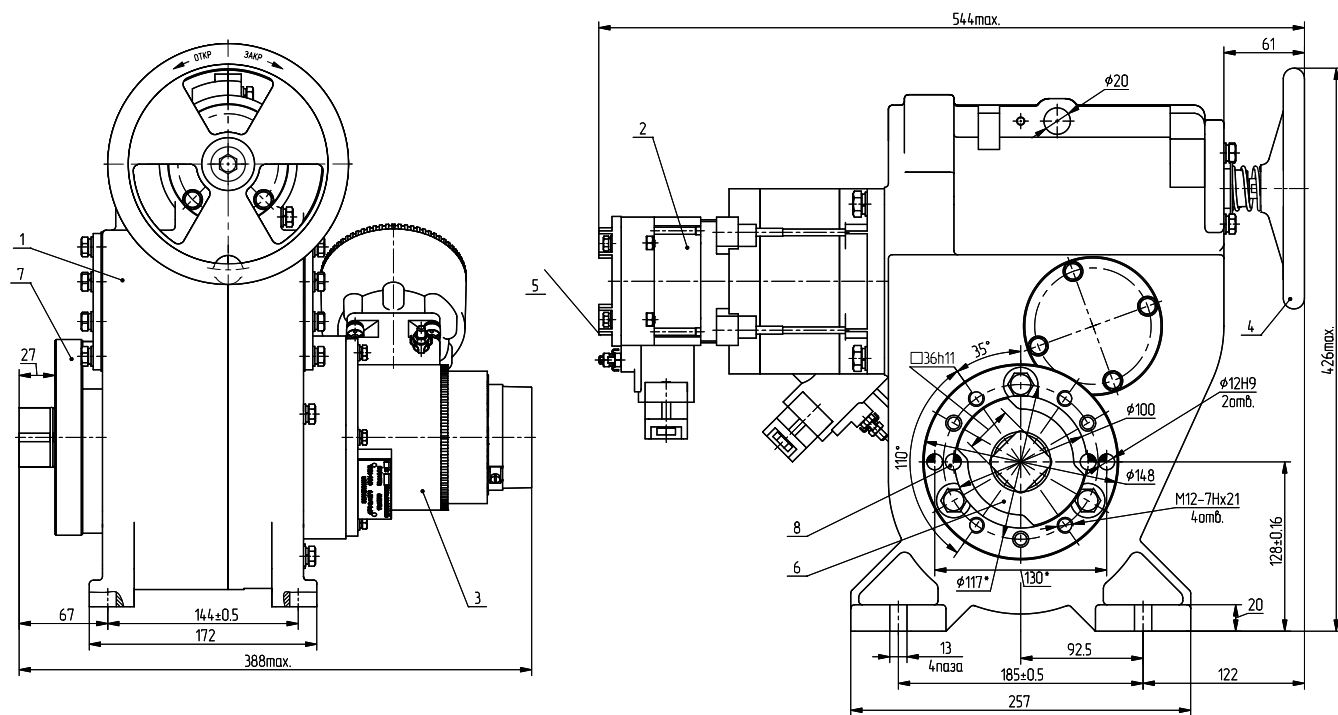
Габаритные и присоединительные размеры М30-250-ИБТ4
